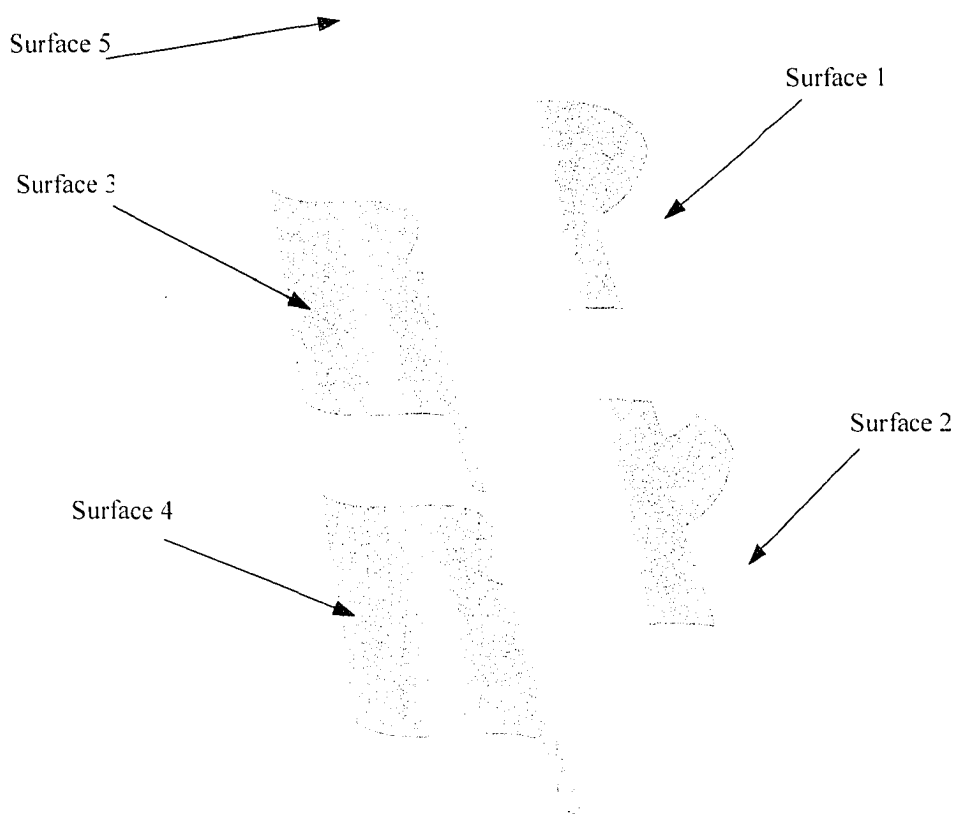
Vue éclatée des surfaces utilisées pour l'alignement
